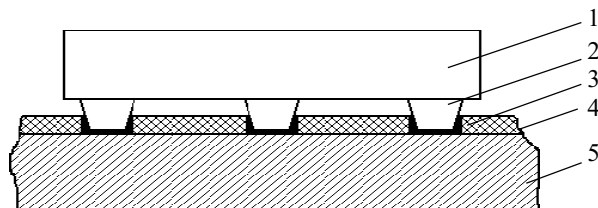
Установка бескорпусного кристалла с объемными выводами на плату:
